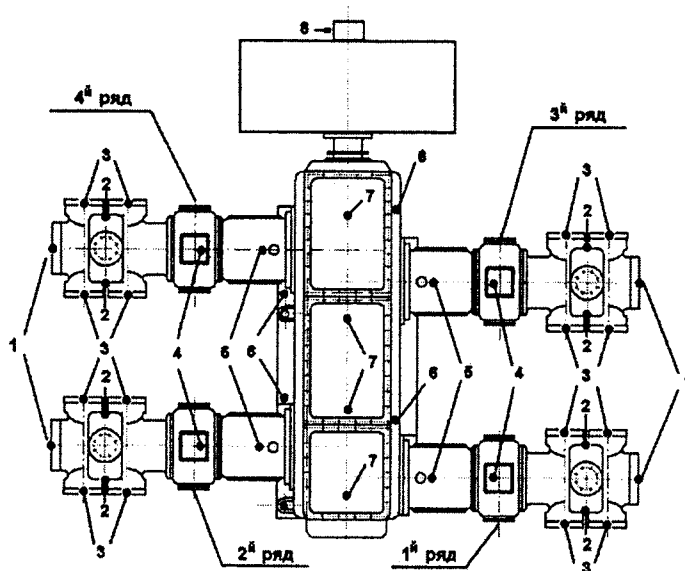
Схема расположения датчиков оппозитного компрессора
